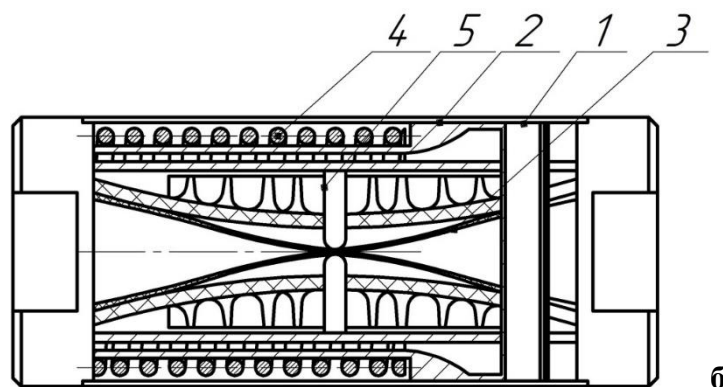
Конструкція нормально закритого пневматичного шлангового затвору: 1 – патрубок подачі стисненого повітря; 2 – корпус; 3 – патрубок з еластичного матеріалу; 4- пружина; 5 – поршень
